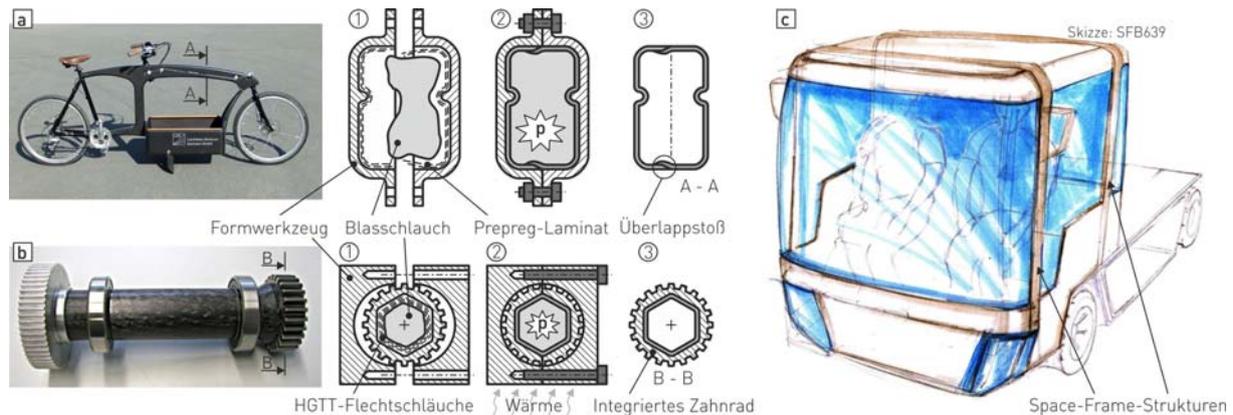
FKV-Hohlstrukturen, gefertigt mittels Schlauchblastechnik: Rahmen für ein Transportfahrrad (a), prototypische Getriebewelle (b) sowie Space-Frame-Konzept für eine Nutzfahrzeug-Kabine (c)
